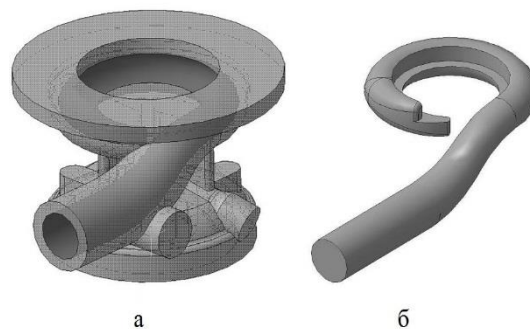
а - 3D-модель корпуса бензинового центробежного насоса, б – песчаный стержень
